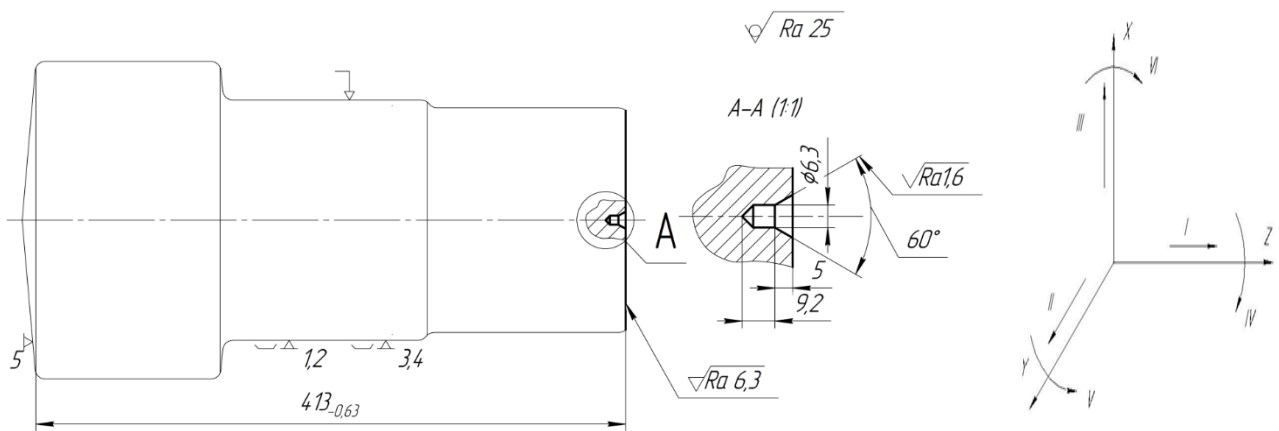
Схема базування на універсально-фрезерній операції 025
